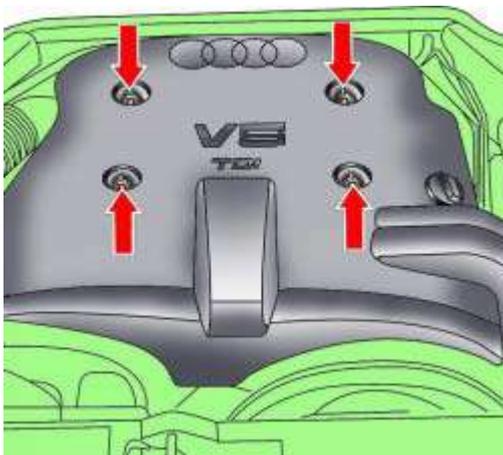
Расположение винтов крепления кожуха двигателя
